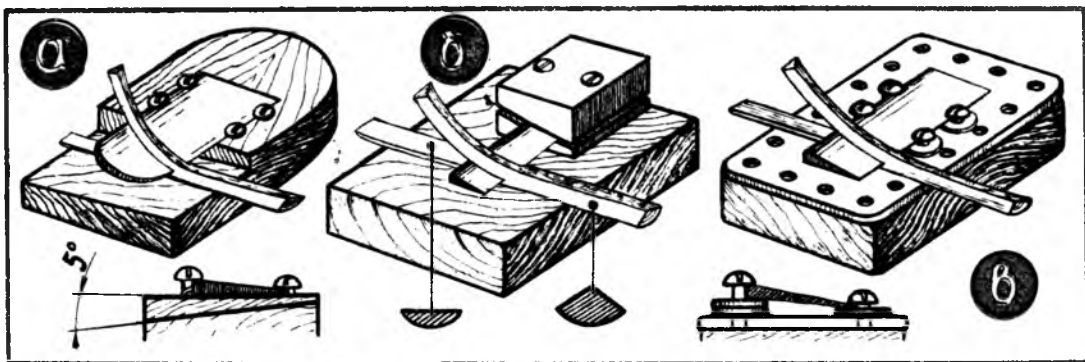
Плоскостный струг (шриф): а — на основе бруска; б — с прижимной колодкой; в — из деталей детского конструктора
